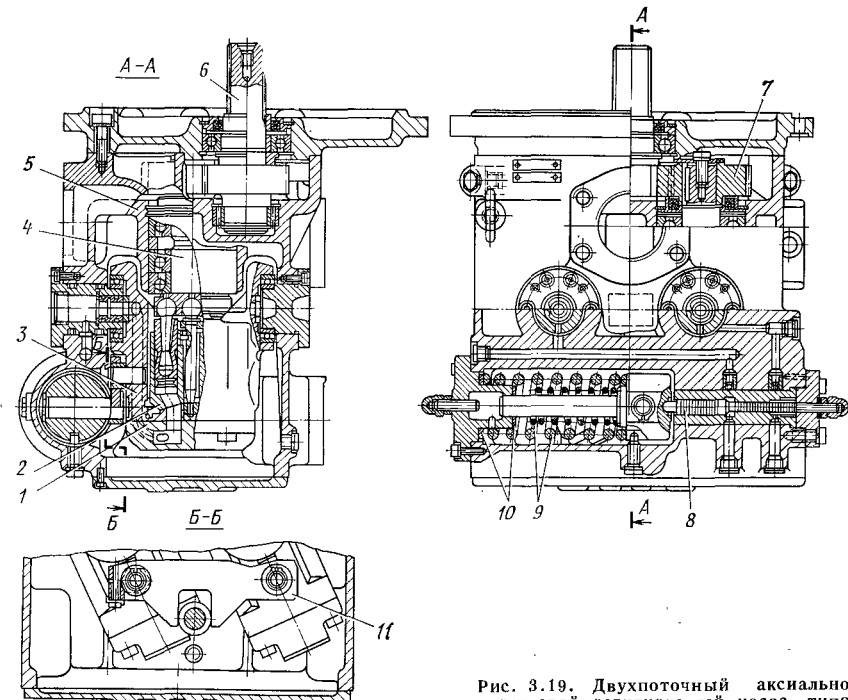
Двухпоточный аксиально-поршневой регулируемый насос типа-размера 223.20 в корпусе из чугуна
